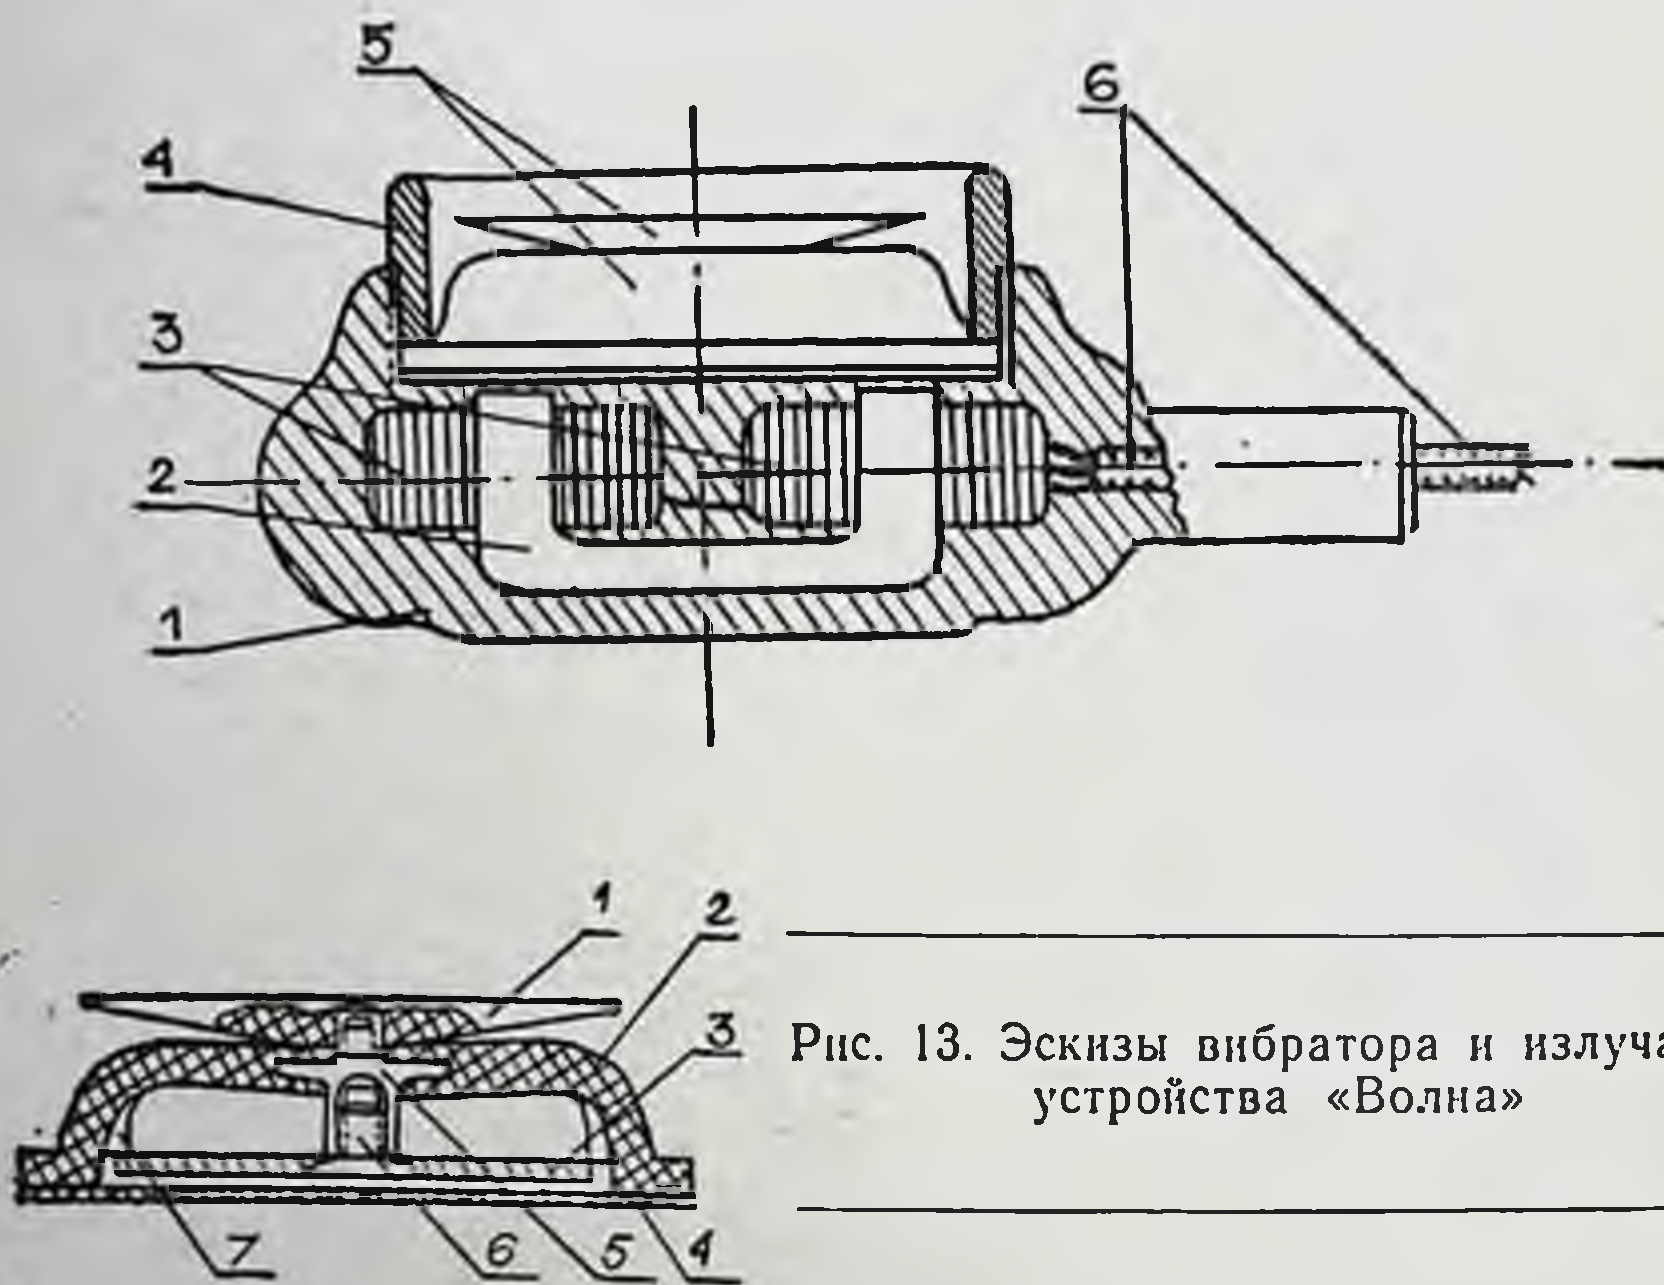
Эскизы вибратора и излучателя устройства «Волна»
